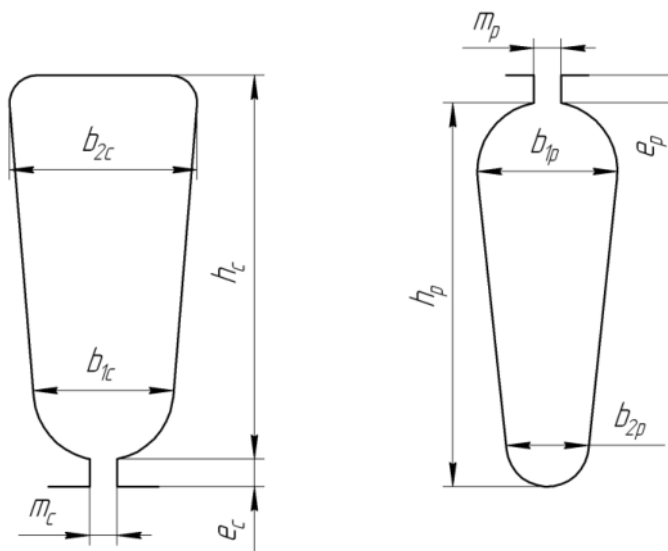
Форма пазов статора и ротора исследуемого двигателя
